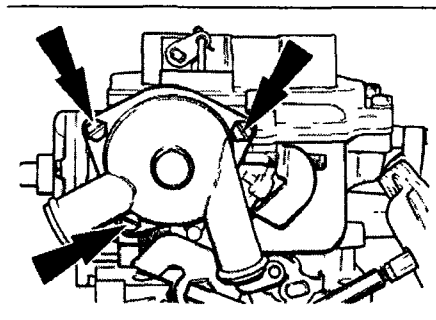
,а. Винты крепления корпуса биметаллической пружины
